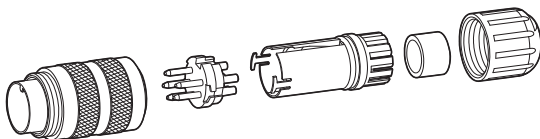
Connettore circolare diritto con bloccaggio a vite per cavo a sezione circolare SWD
